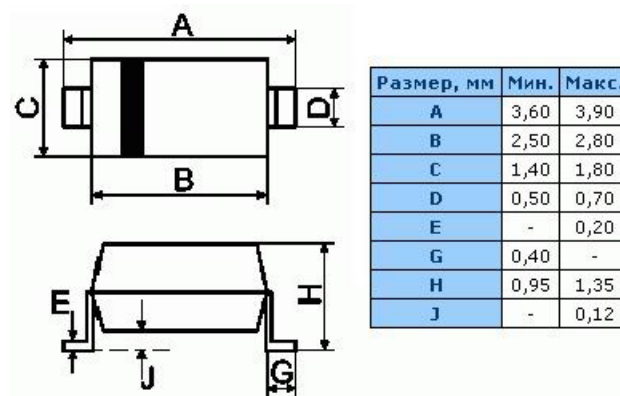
Внешний вид и габаритные размеры корпуса SOD-123
